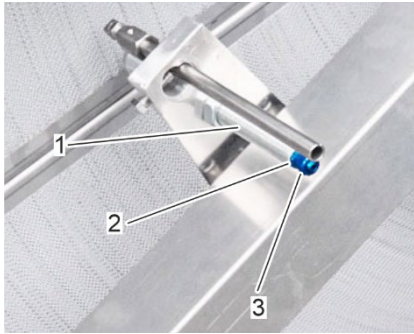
Tuerca de unión de la boquilla de aire comprimido
